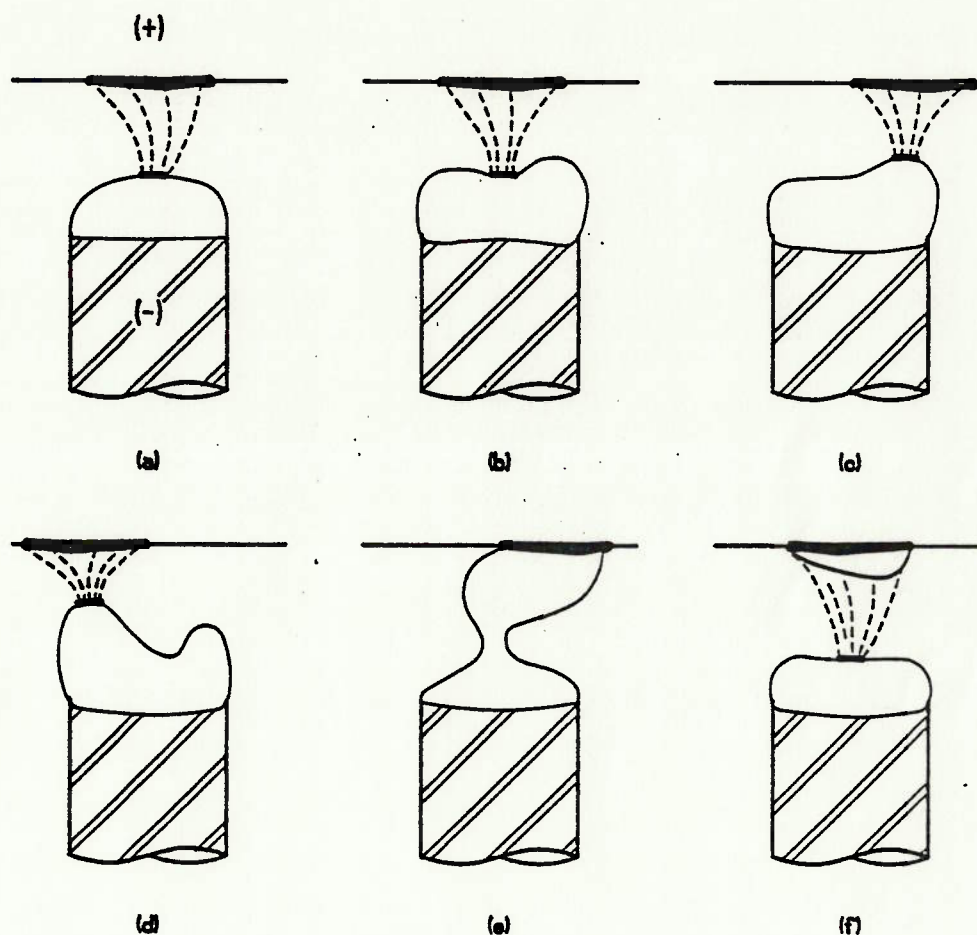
Mecanismo de transferência metálica segundo Conrady [33] para a soldagem com eletrodo nú em CCFD na posição sobre-cabeça.
